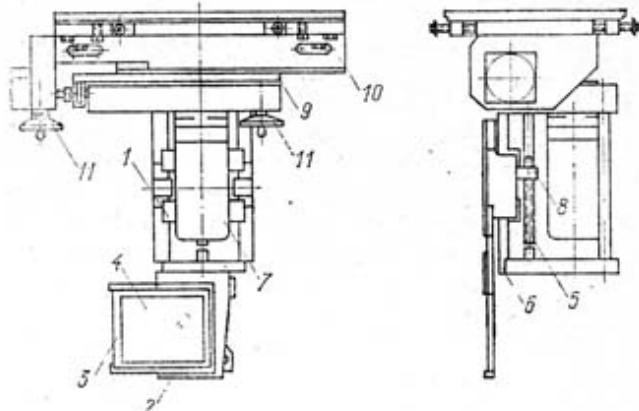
Механизм двухкоординатного перемещения голографического блока памяти: 1 — каретка вертикального перемещения, 2 — скоба, 3 — кассета, 4 — голографический блок памяти, 5 — винт, 6 — направляющие, 7 — шаговый двигатель, 8 — гайка, 9 — каретка горизонтального перемещения, 10 — основание, 11 — маховики
